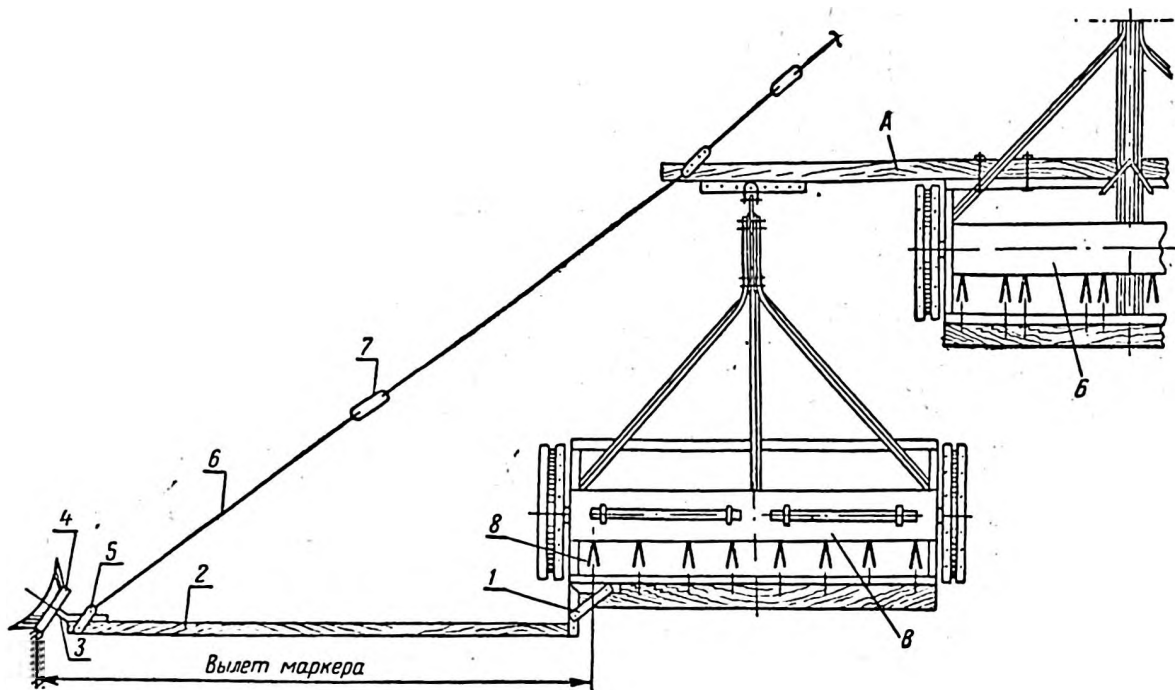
Схема колесно-дискового маркера (вид сверху):
